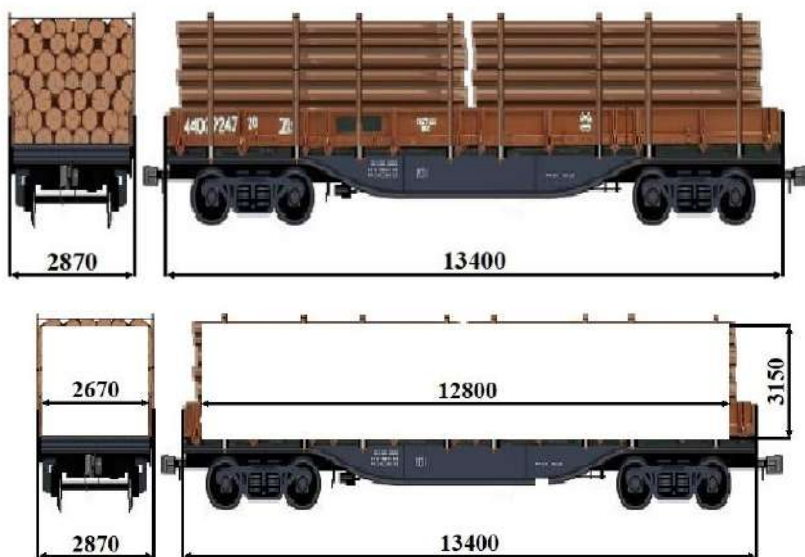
Габаритные размеры внутренней части для скрытного перемещения ВВСТ
